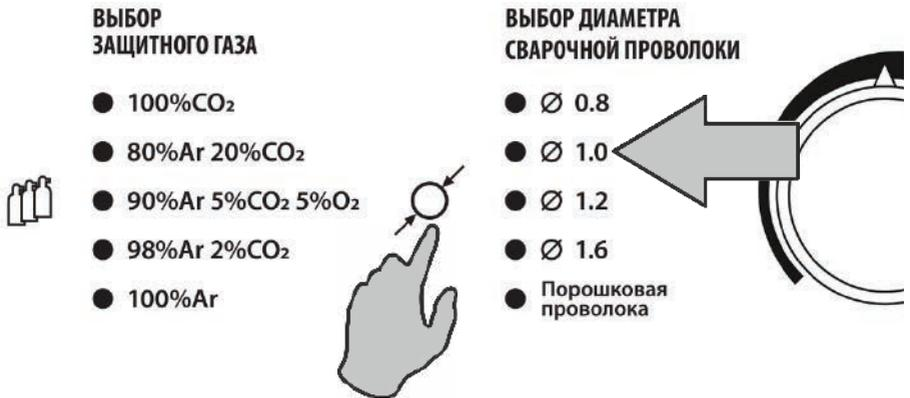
Выбор диаметра сварочной проволоки.
